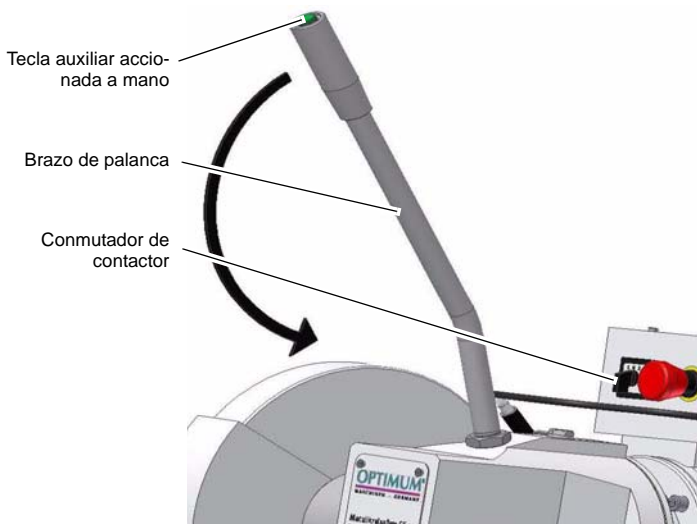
Tecla auxiliar accionada a mano y Conmutador de contactor
